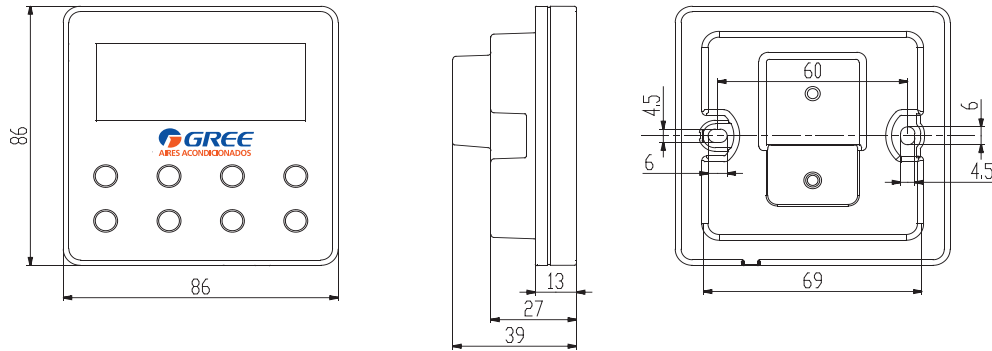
Dimensiones del controlador de zona (Unidades:mm)
